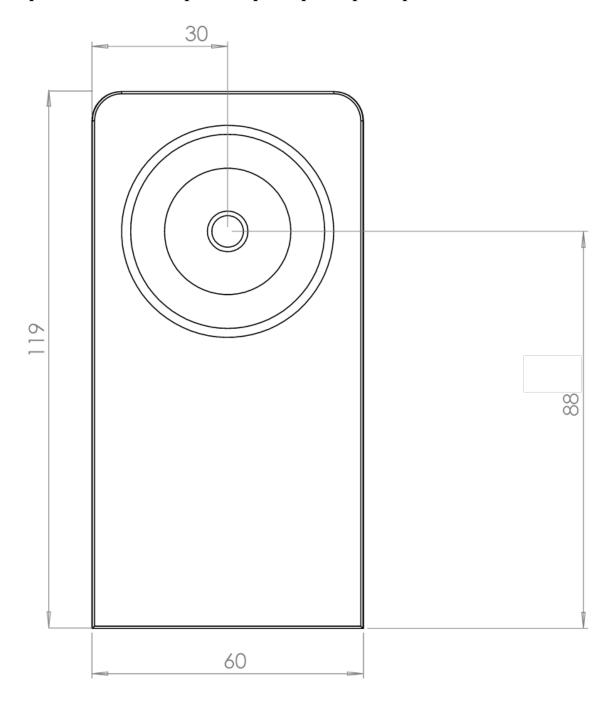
Габаритные размеры пирометра. Вид спереди.
